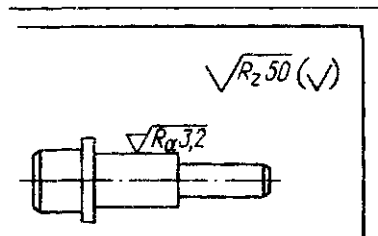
Обозначение шероховатости, одинаковой для части поверхностей изделия
